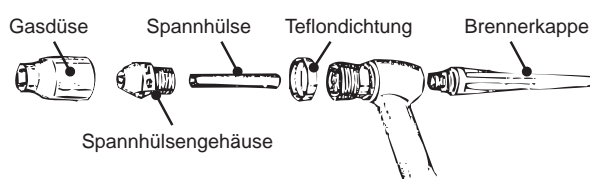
Explosionsschaubild des WIG-Schweißbrenners
